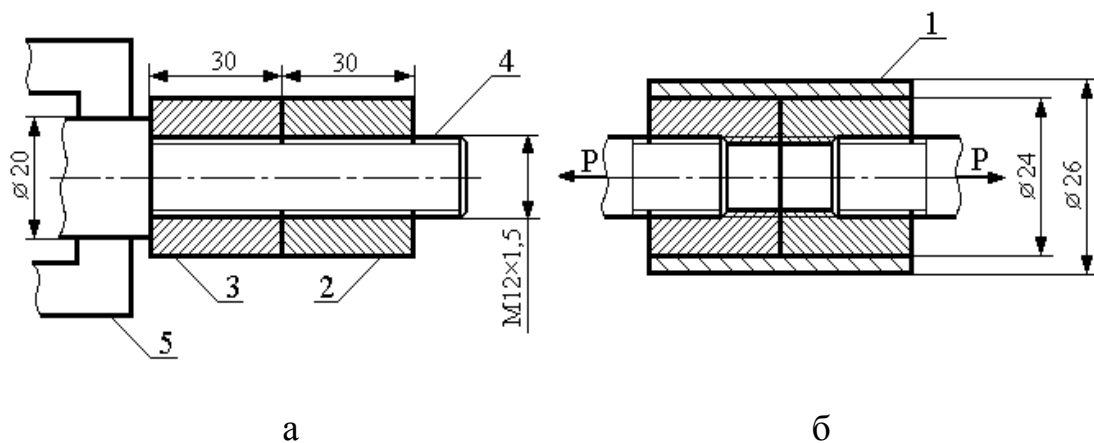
Схема визначення когезійної міцності покриттів: а – схема підготовки зразка; б – схема випробування; 1 – шар покриття; 2, 3 – втулки, що мають внутрішню різьбу; 4 – центрувальний гвинт; 5 – патрон обертача
